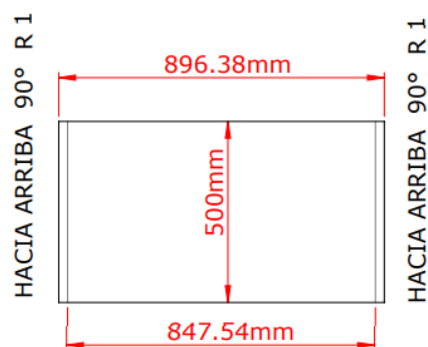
Sección 3 de la carcasa - Detalle de las medidas
